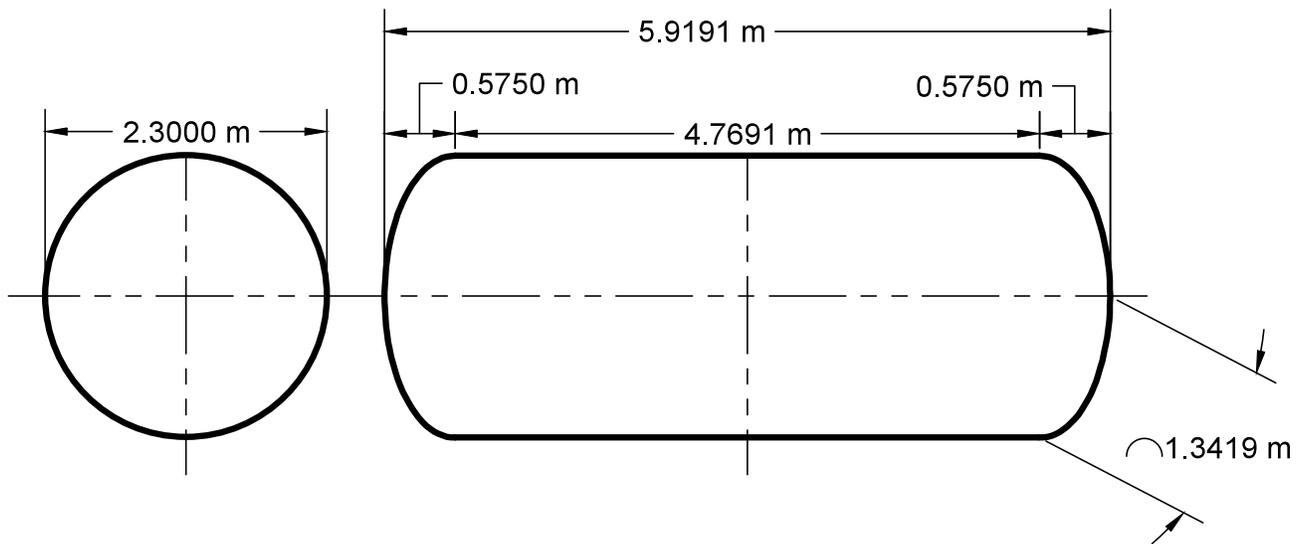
Dimensiones calculadas del recipiente diseñado
